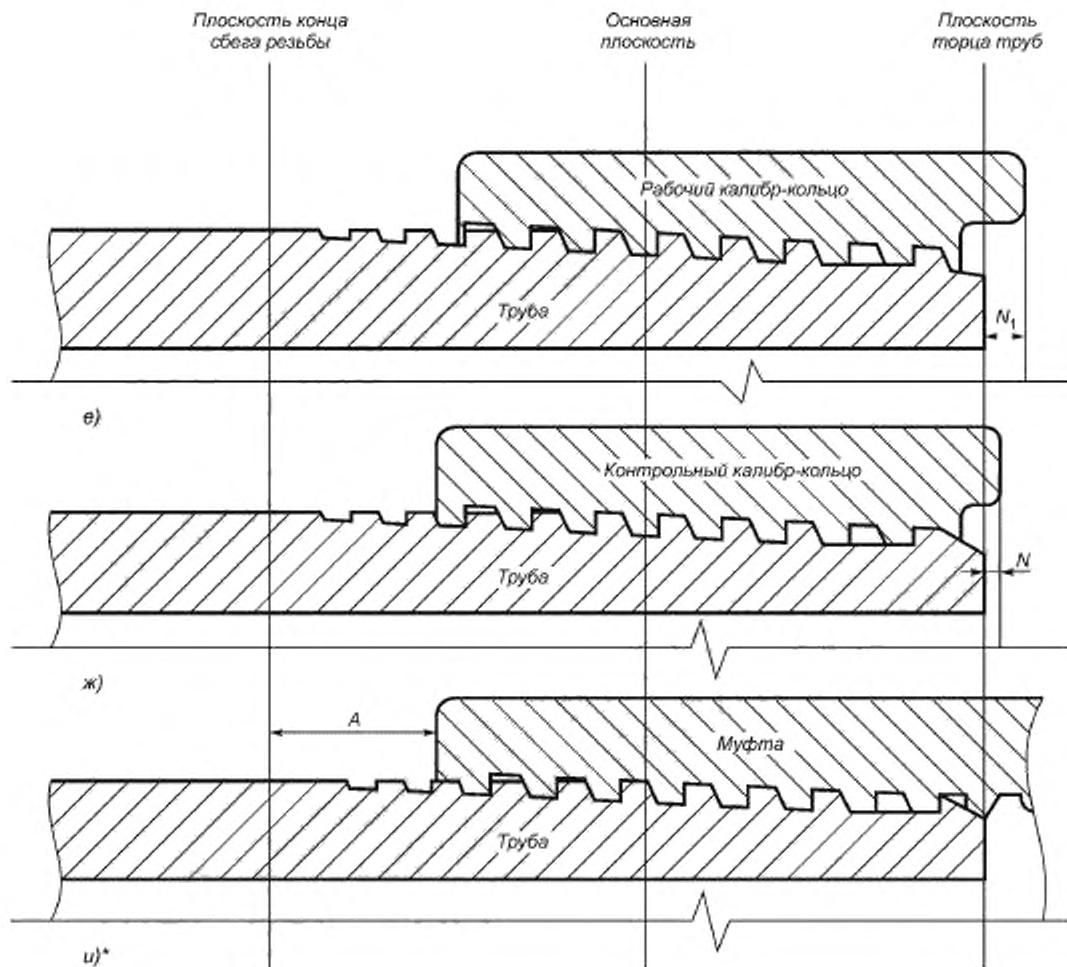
Схема взаимосвязи между контрольными калибрами, рабочими калибрами и резьбой изделий с резьбовым соединением ВС
